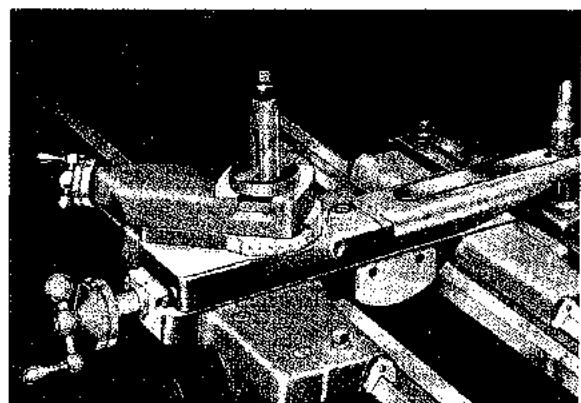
Soporte orientable para torneado en ángulo y para mecanizar conos cortos (South Bend Lathe Works).
